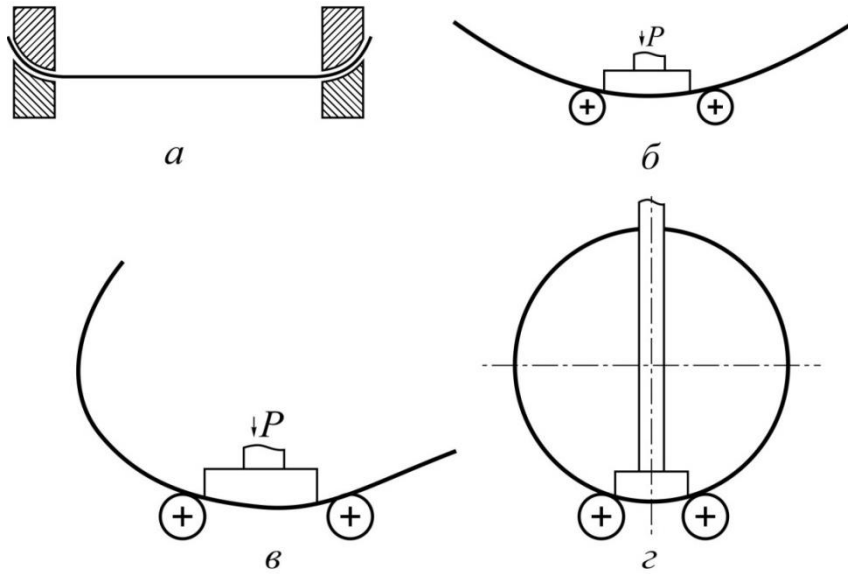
Схемы формовки трубы из плоской заготовки
